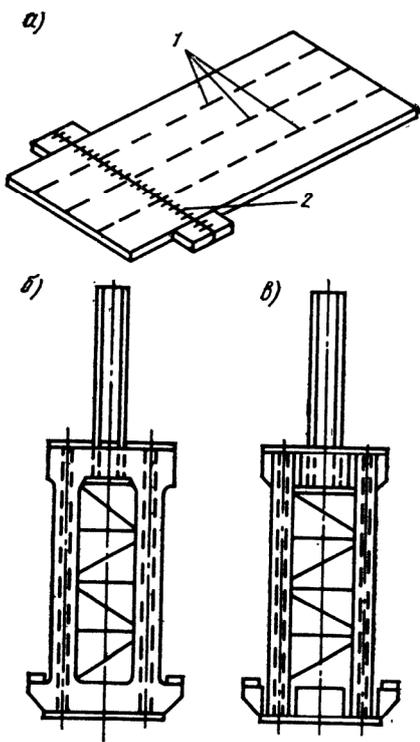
Примеры конструктивных решений, позволяющих расширить область применения автоматической сварки
